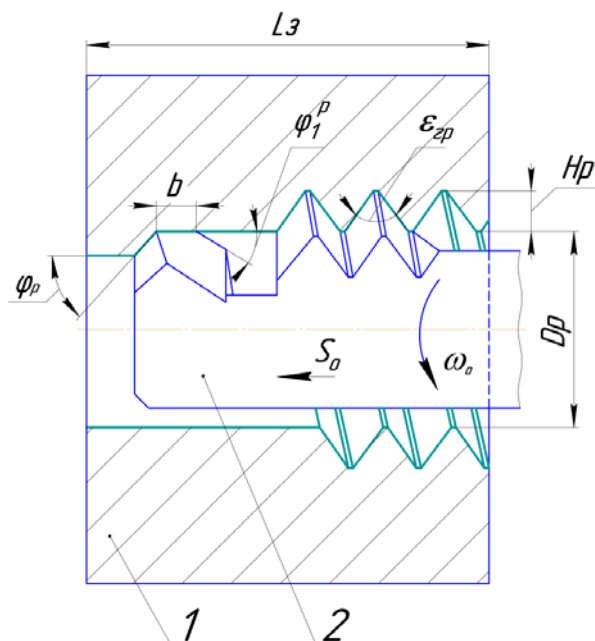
Схема нарезания внутренней резьбы комбинированным инструментом резцом-гребёнкой
